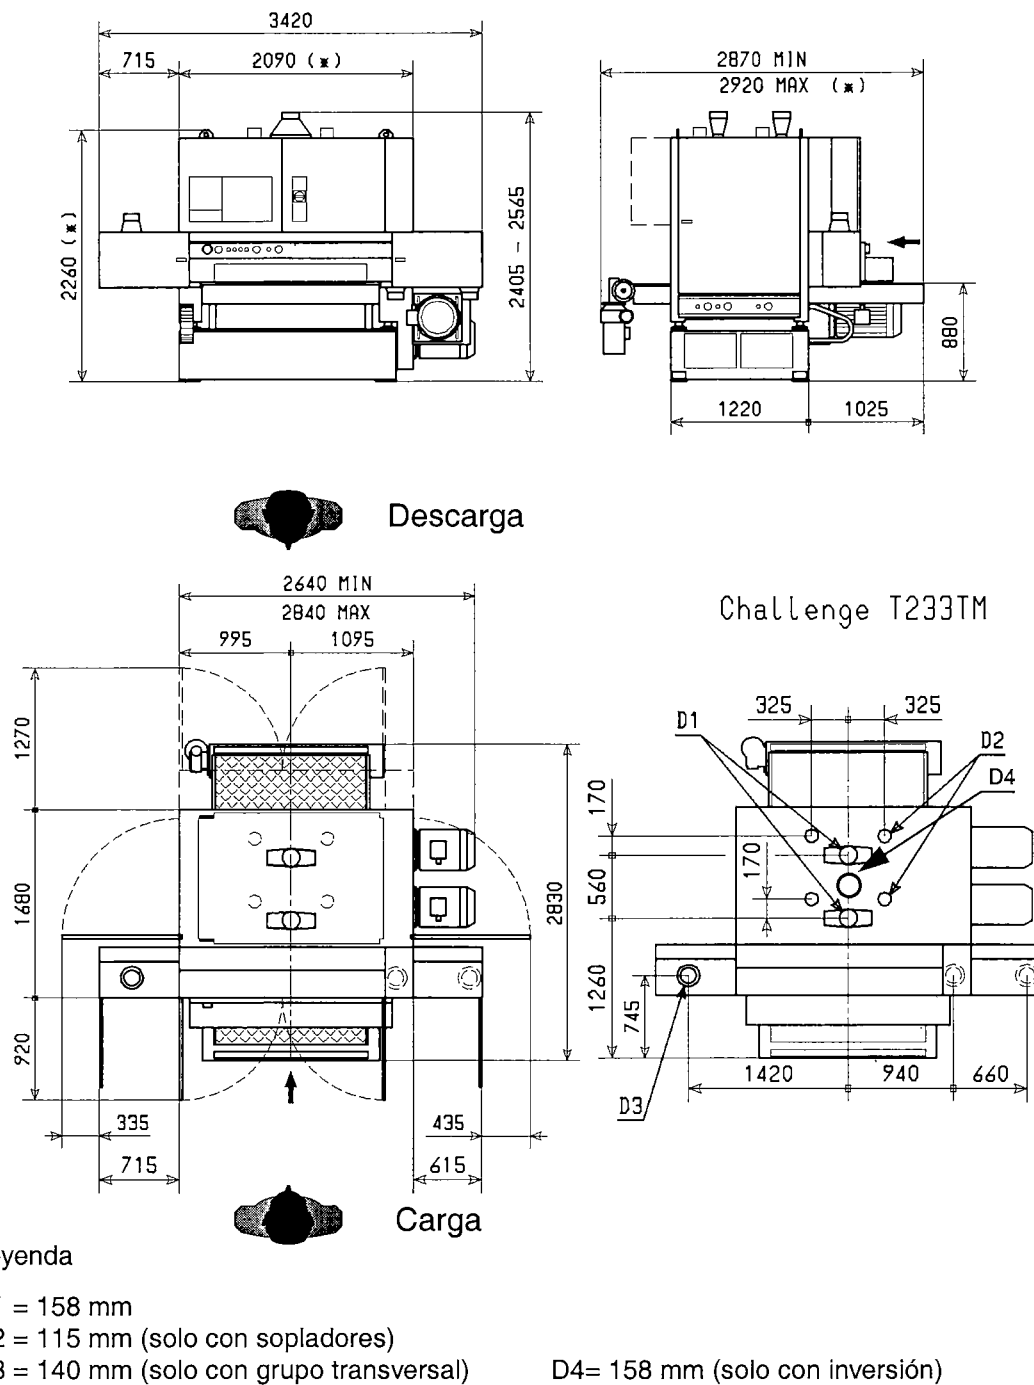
a Espacio ocupado y dimensiones de la máquina
